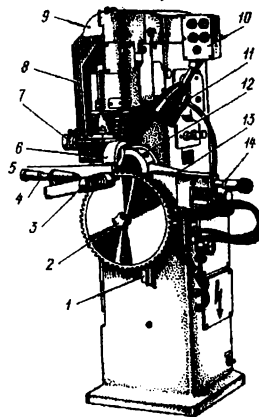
Станок Т4ПТ4 для заточки зубьев круглых пил, оснащенных пластинками твердого сплава
